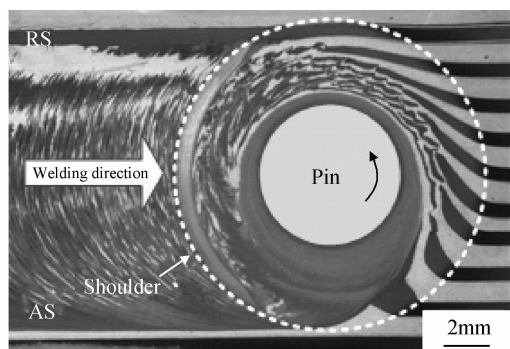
平行焊缝排列焊后焊缝表面材料流动宏观形貌
